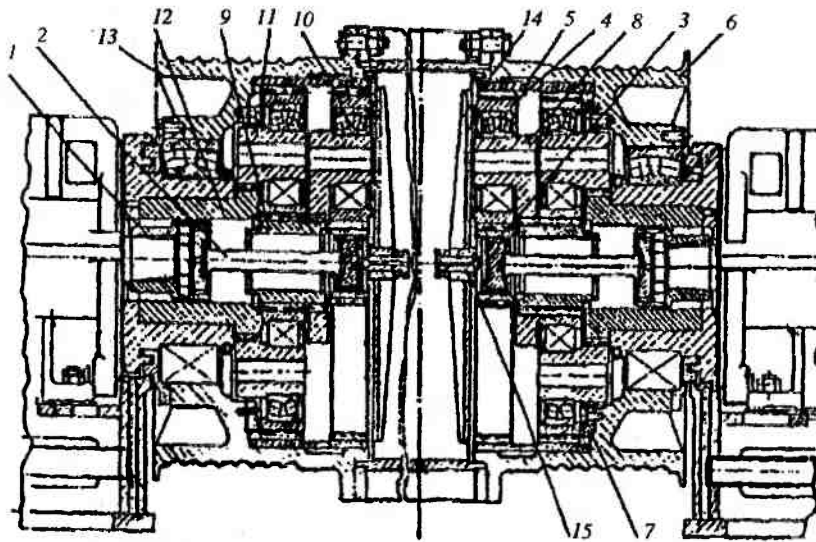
Планетарный барабан-редуктор подъемной лебедки экскаватора ЭКГ-10
